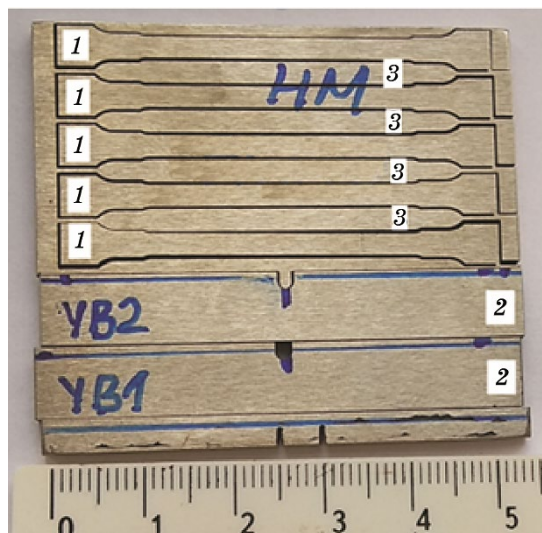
Приклад схеми розкрою механічно обробленої заготовки нагрітого металу «вертикальна стінка» за виготовлення зразків для механічних випробувань електроерозійною різкою. Позначення видів зразків: 1 — зразок для випробувань на повздовжній статичний розтяг, 2 — зразок для випробувань на ударне загинавання, 3 — зразок для випробувань на статичне загинавання.
